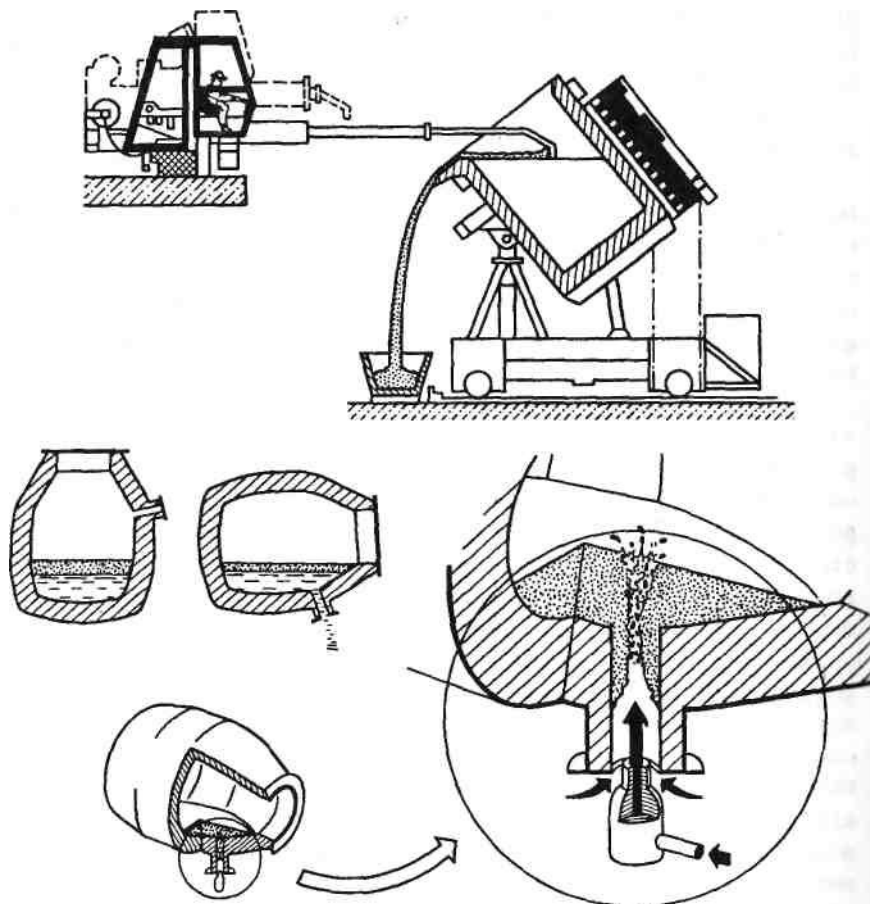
Установка для скачивания шлака с поверхности металла в ковше
